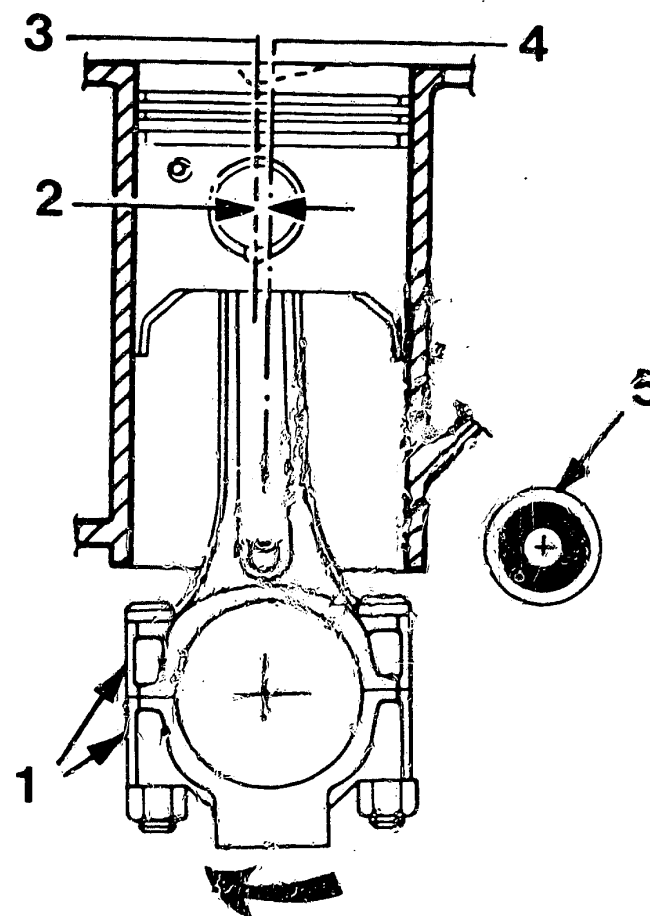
Anordnung von Kolben, Pleuel und Nockenwelle beim 1116- und 1301-cm³-Motor. Der Pfeil zeigt die Drehrichtung des Motors von der Steuerseite her. 1 Nummer des Zylinders, zu dem die Pleuelstange gehört – 2 Achsversatz des Kolbens um 2mm – 3 Bolzenachse – 4 Zylinderachse – 5 Nebenantriebswelle.
